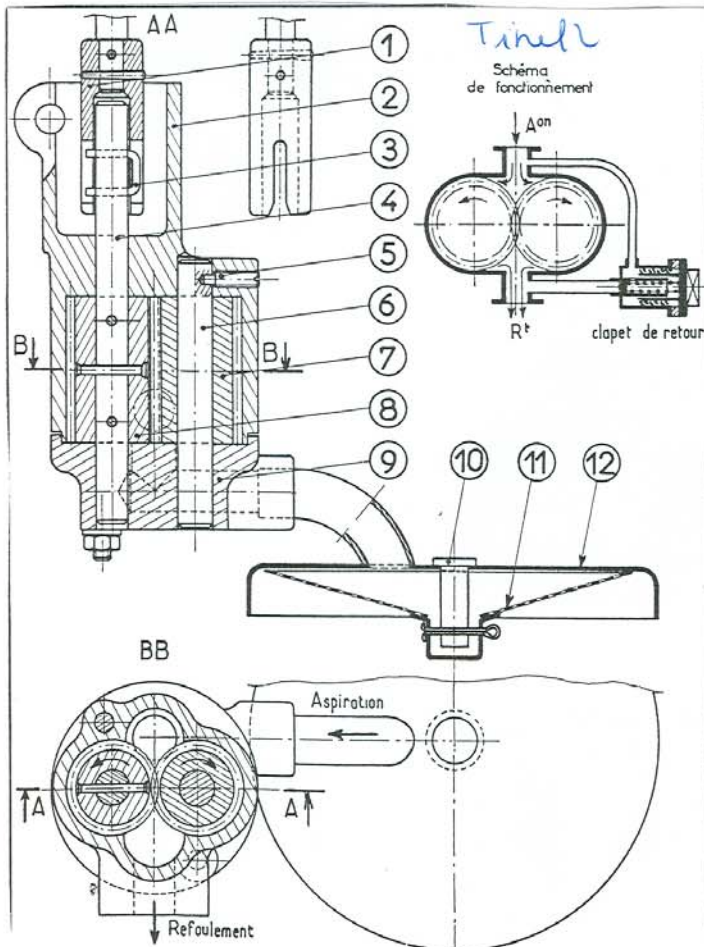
Pompe à engrenage de moteur d'automobile.
